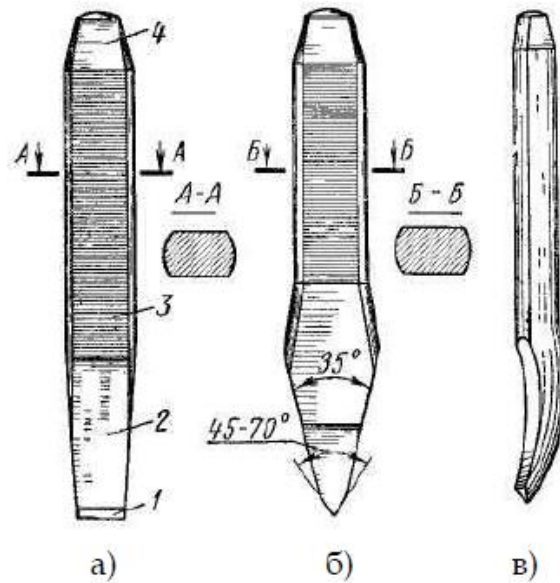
Інструменти для рубання: а – зубило; б – крейцмейсель; в – канавочник
